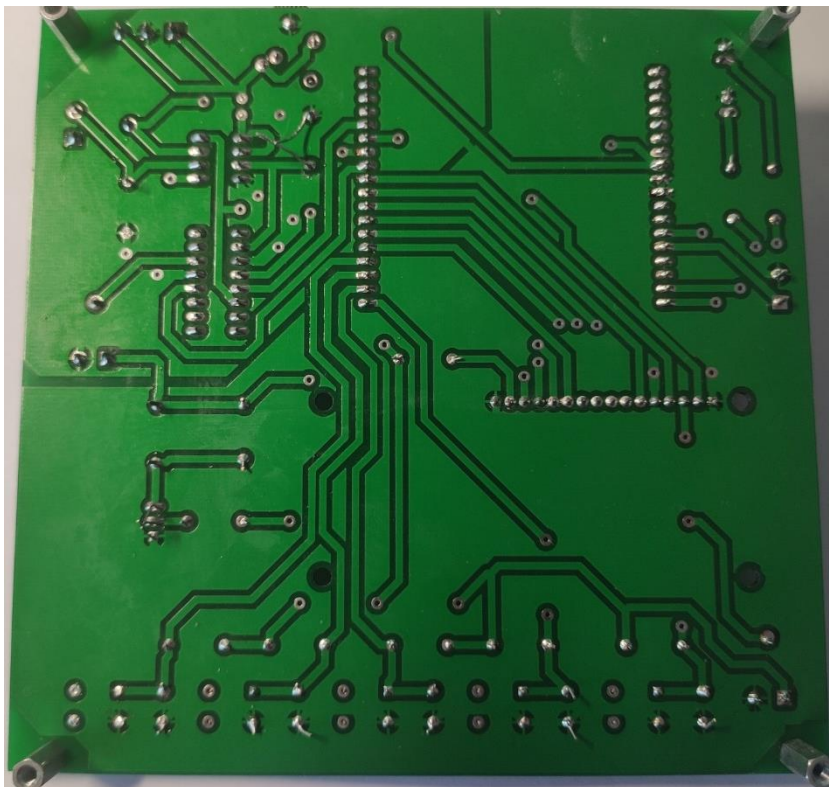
Estat de la cara inferior un cop realitzat el procés de soldadura.
